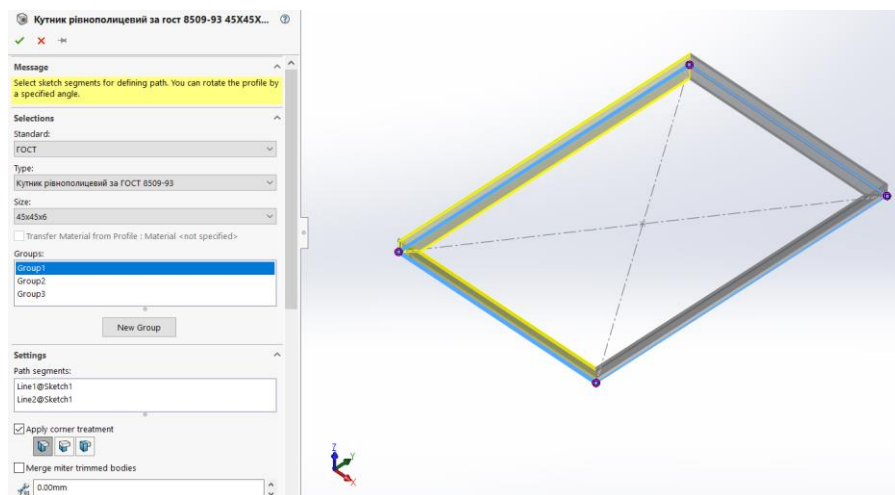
Створення зварної конструкції в середовищі модуля Weldments.
